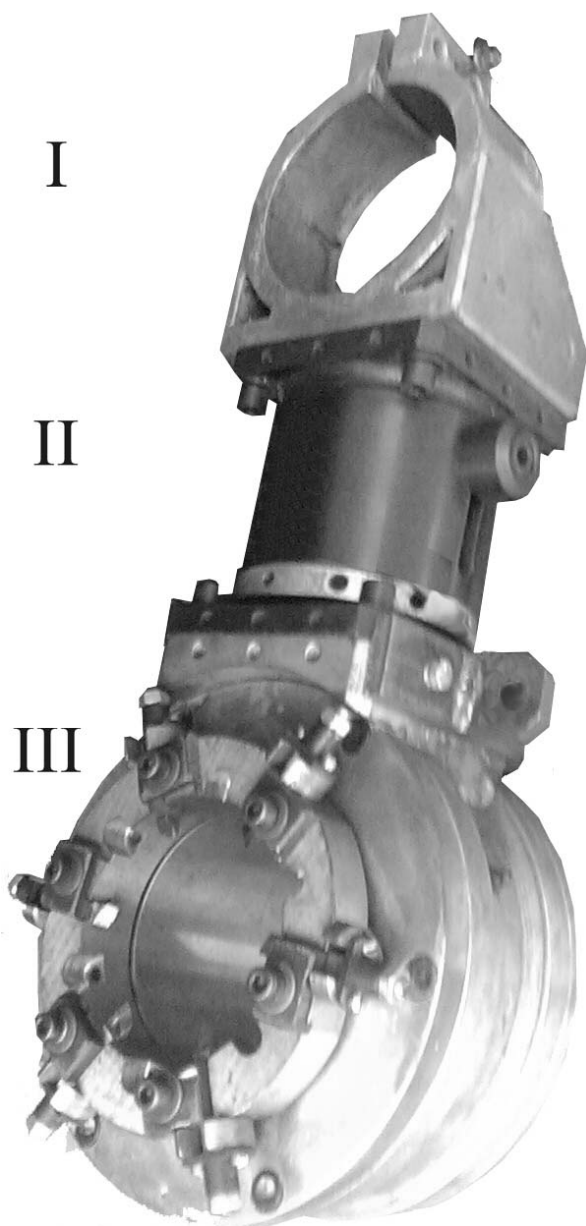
Пристрій для модернізації вертикально-фрезерного верстата мод.6Р10
